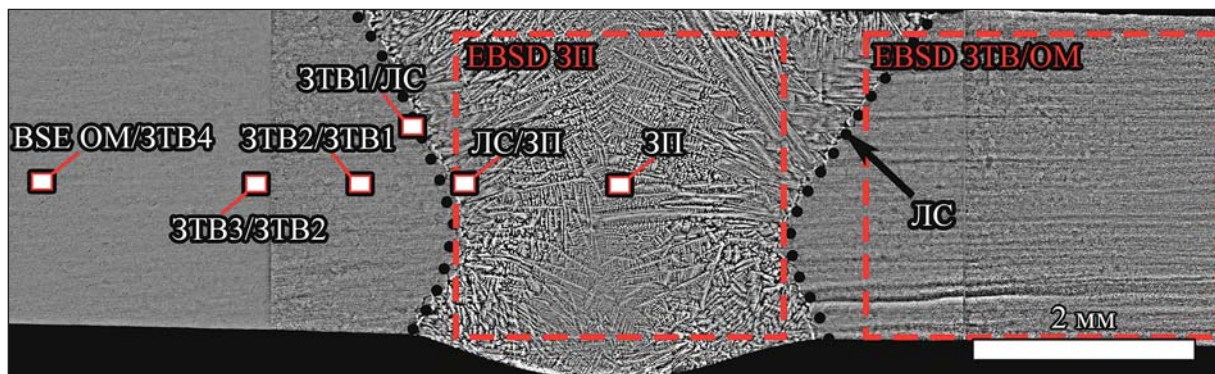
Поперечное сечение сварного шва сплава ВТИ-4, полученного плазменной сваркой проникающей дугой, с разметкой областей съемки BSE- и EBSD-анализов (см. рис. 5 и 6)
